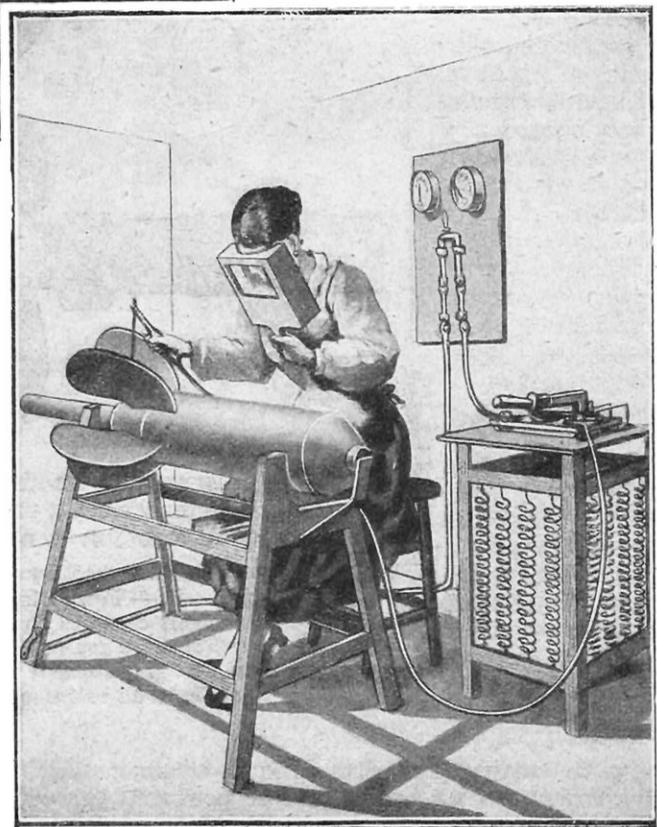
SOUDURE DES AILETTES SUR UNE TORPILLE
